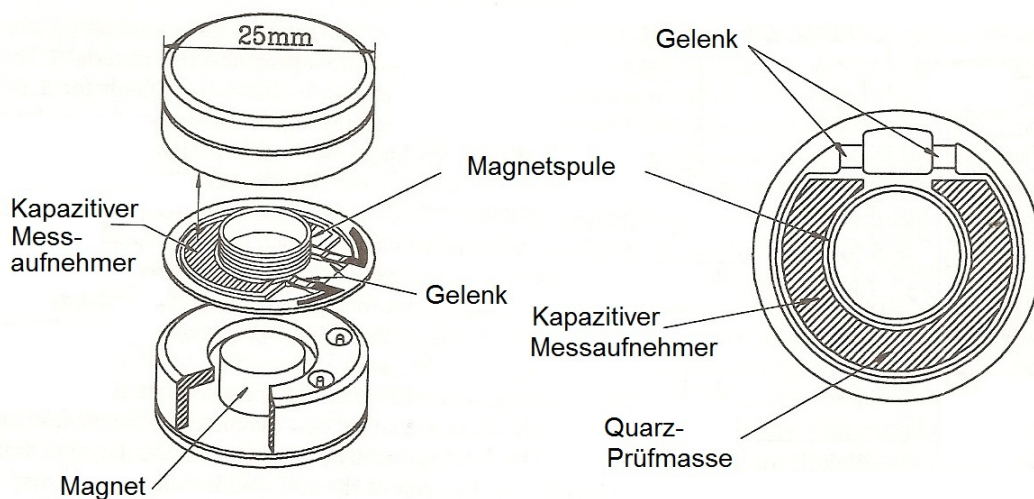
Explosionsgrafik(links) und Schnitt(rechts) eines Beschleunigungssensors mit Q-Flex-Design [Law92]
